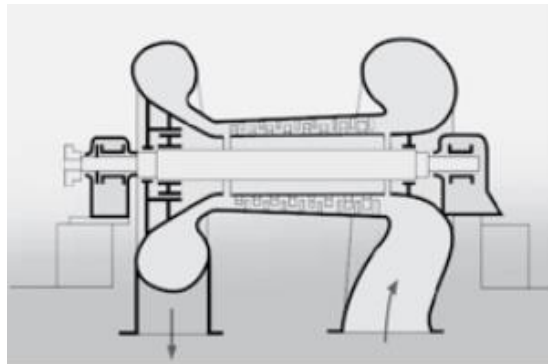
Compresor axial. Fuente: Junta de Castilla y León.
